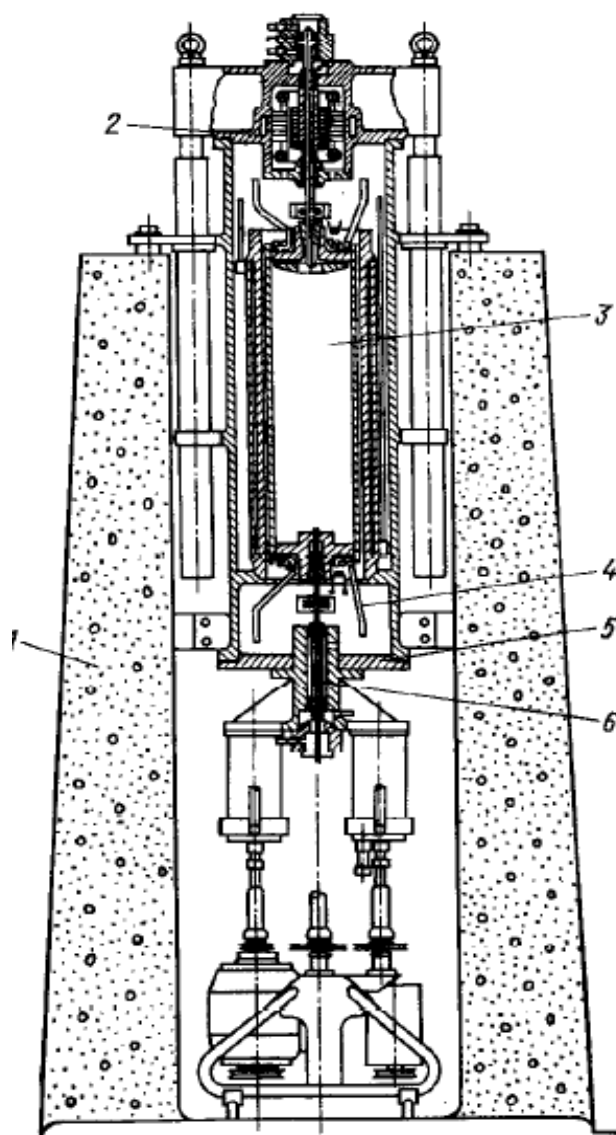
Вертикальный разрез центрифуг Грота (ZG-3 и ZG-5) с жестким ротором: 1 – фундамент; 2 – электропривод; 3 – ротор; 4 – подводка к нижнему электронагревателю; 5 – корпус центрифуги; 6 – нижний подшипник с демпфирующим устройством
